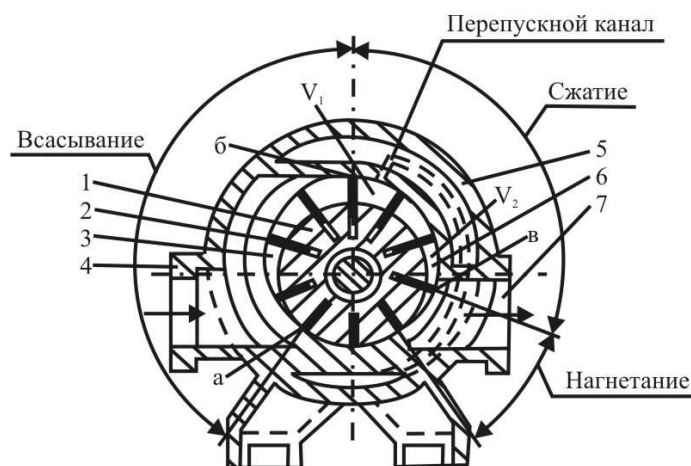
Ротационный компрессор с катящимся ротором:
